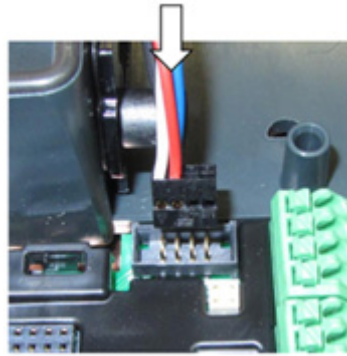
Anschlussstecker auf Steuerplatine einstecken
